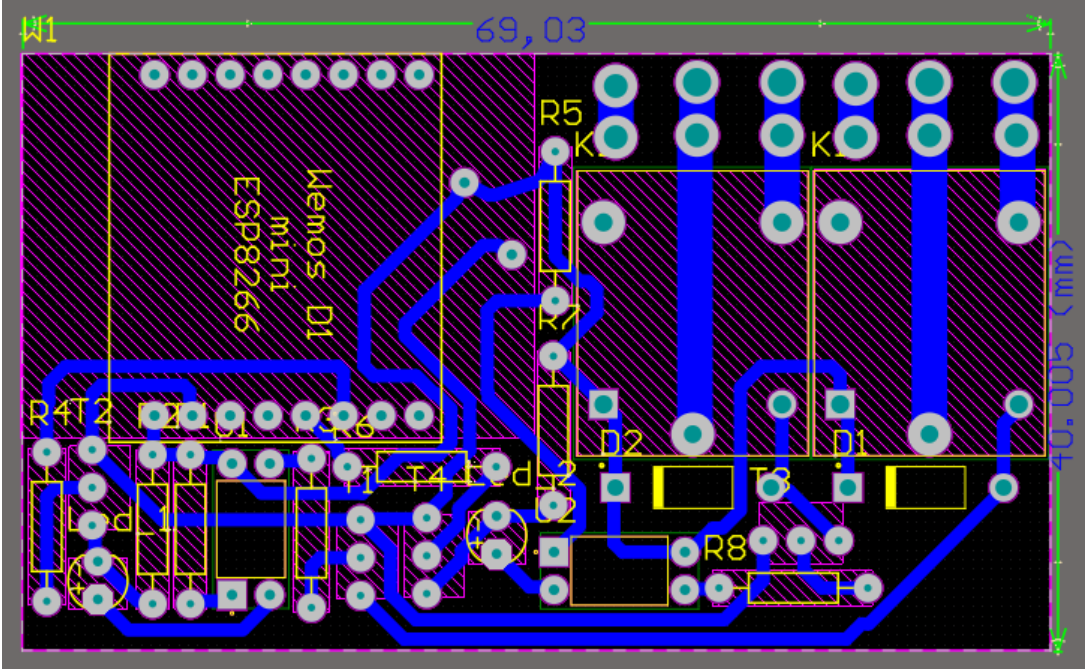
Dimensiones Placa PCB módulo Tomacorriente.
